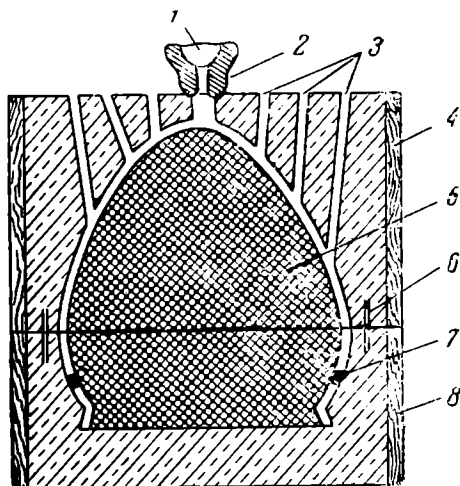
Литейная форма для отливки котлов (реконструкция)
